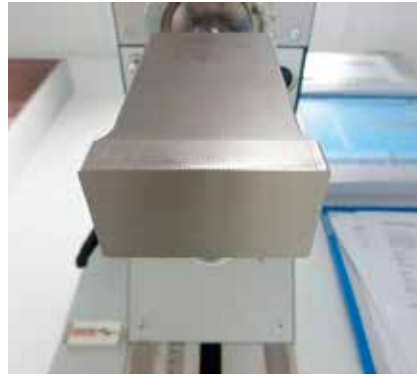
Die Oberfläche des Schweißwerkzeugs (Sonotrode) muss sehr fein geschliffen und poliert werden, um unerwünschte Schmelze- oder Partikelbildung zu verhindern
